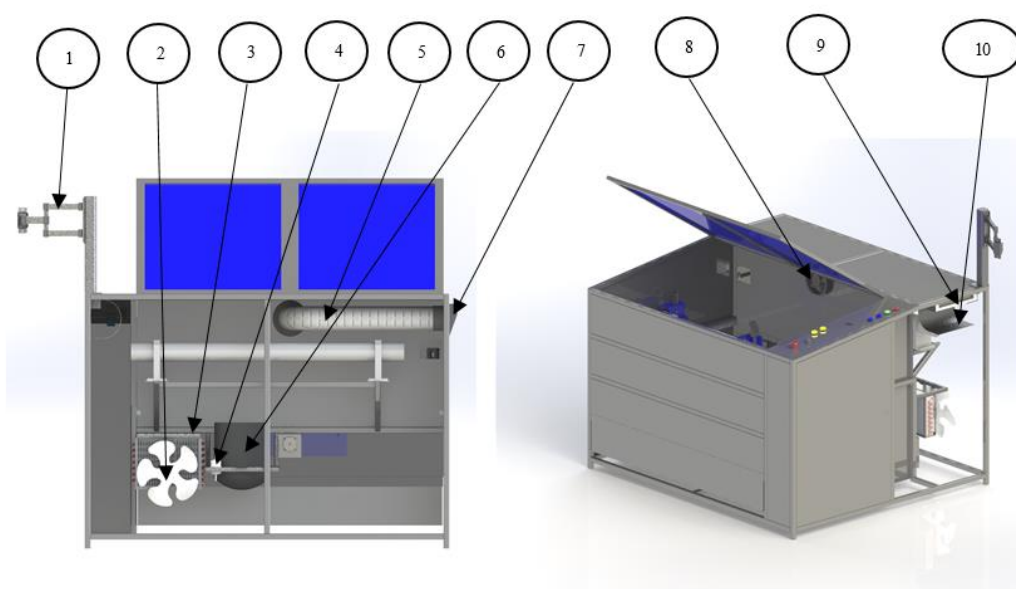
Descripción de componentes de la plataforma CNC de corte por láser
